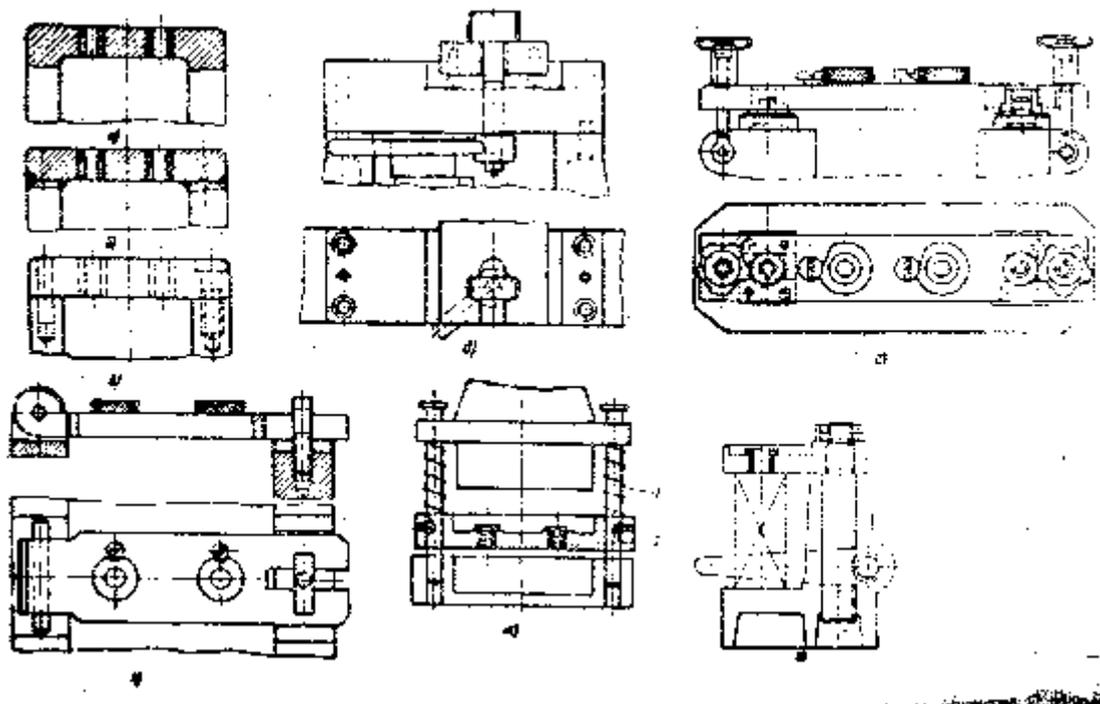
Кондукторные плиты сверлильных приспособлений.
